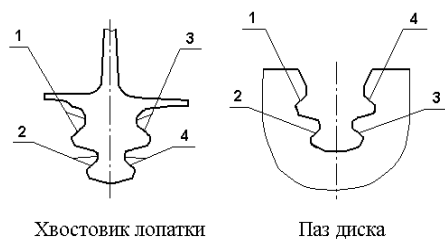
Обозначение поверхностей хвостовика лопатки и паза диска (вид со стороны входа)
